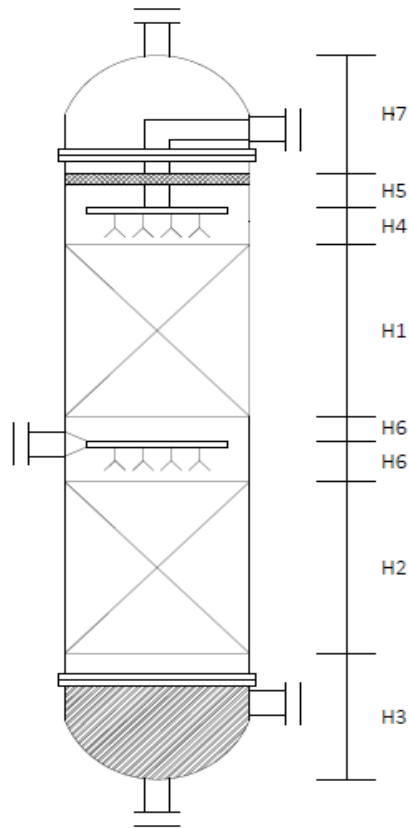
Esquema dimensionat preliminar de la columna DC-301
